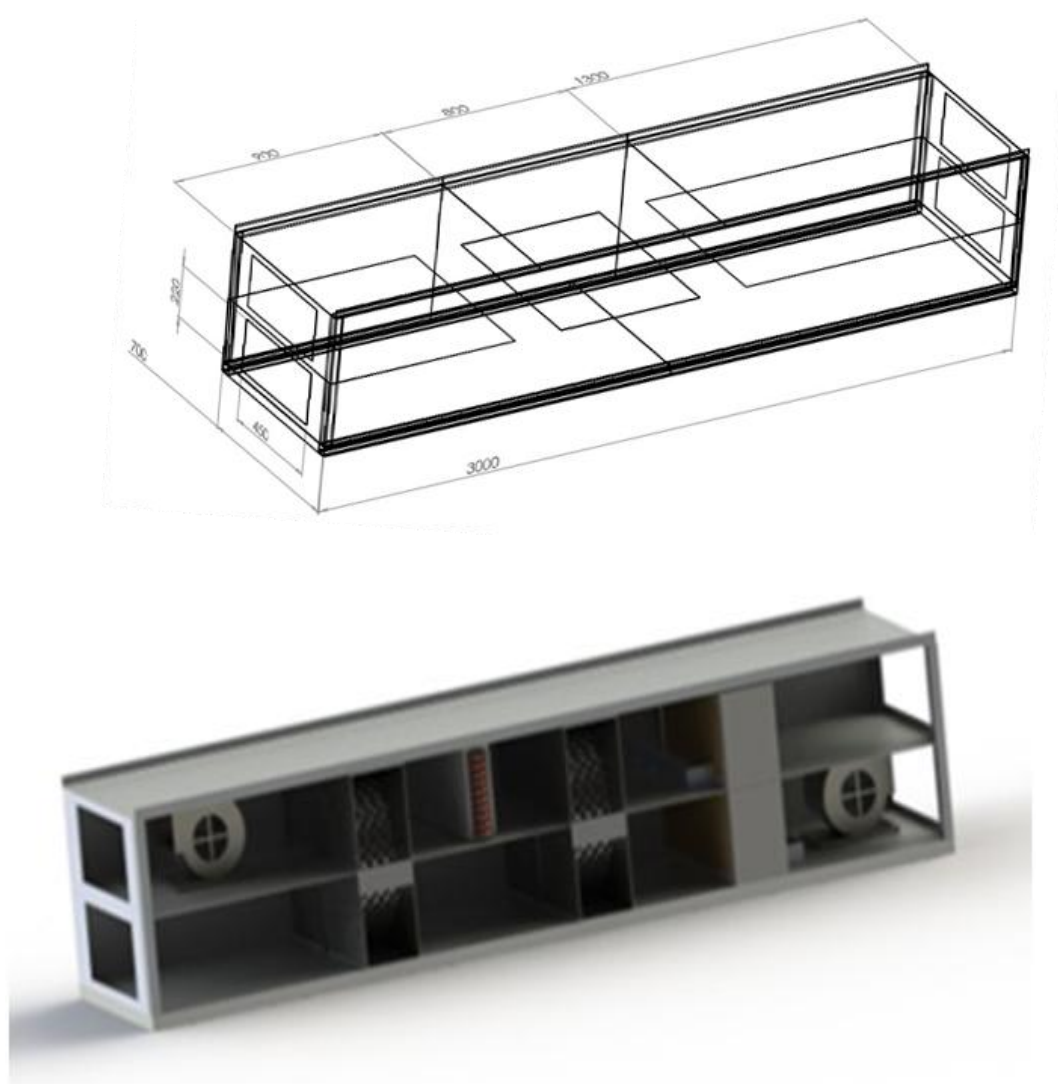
Plan du caisson du système de rafraîchissement à roue de dessiccation.
